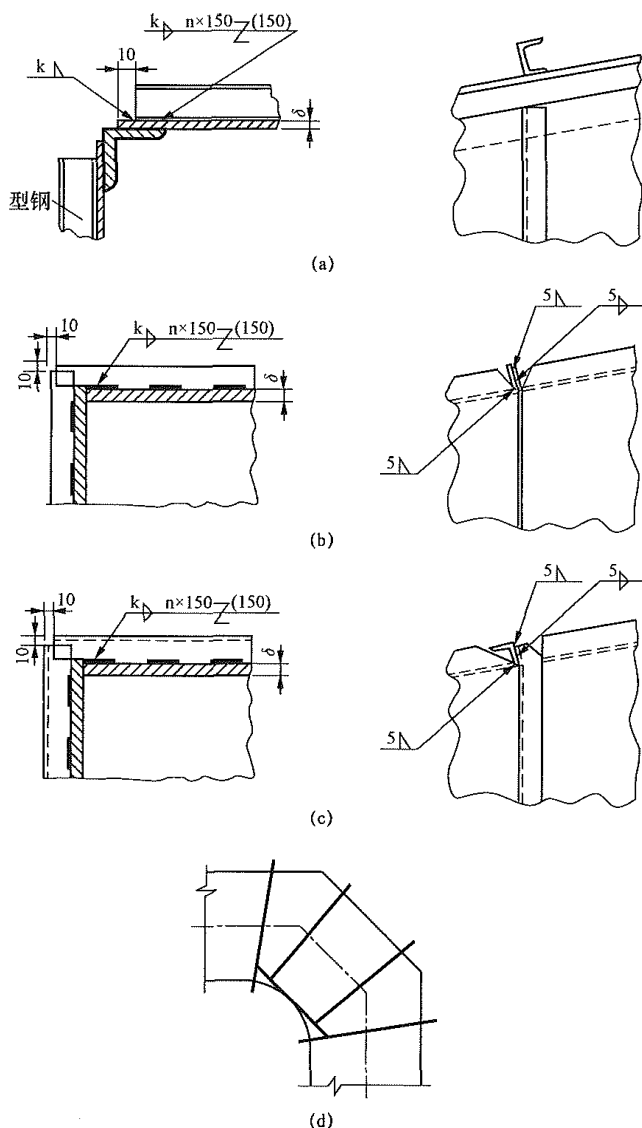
异形道体的加固肋焊接 (mm)
